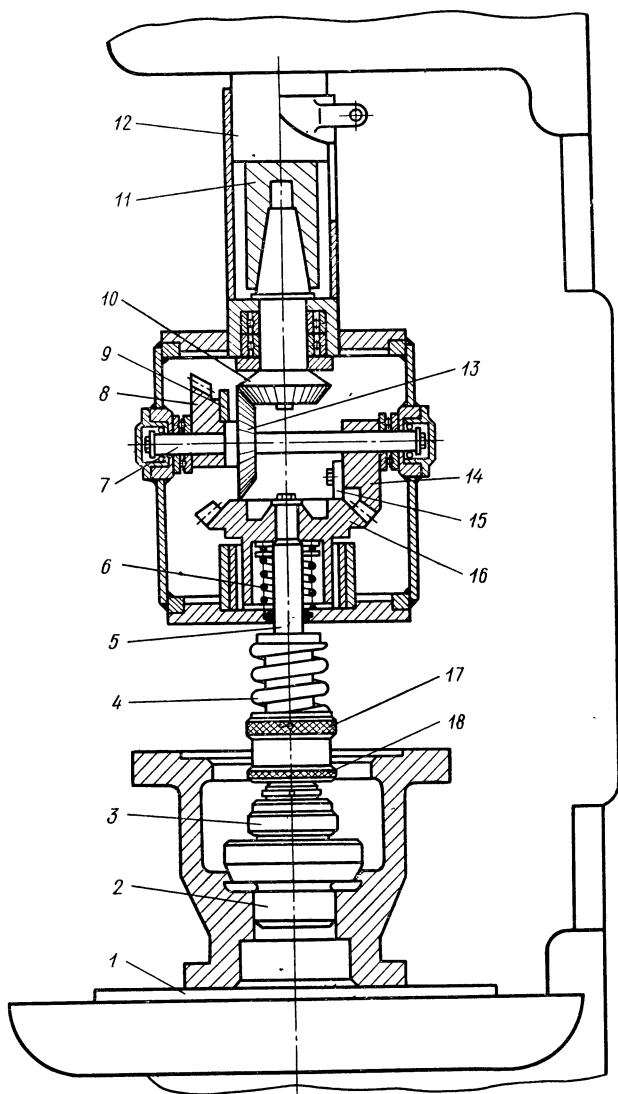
Устройство головки для притирки деталей на вертикально-сверлильном станке:
